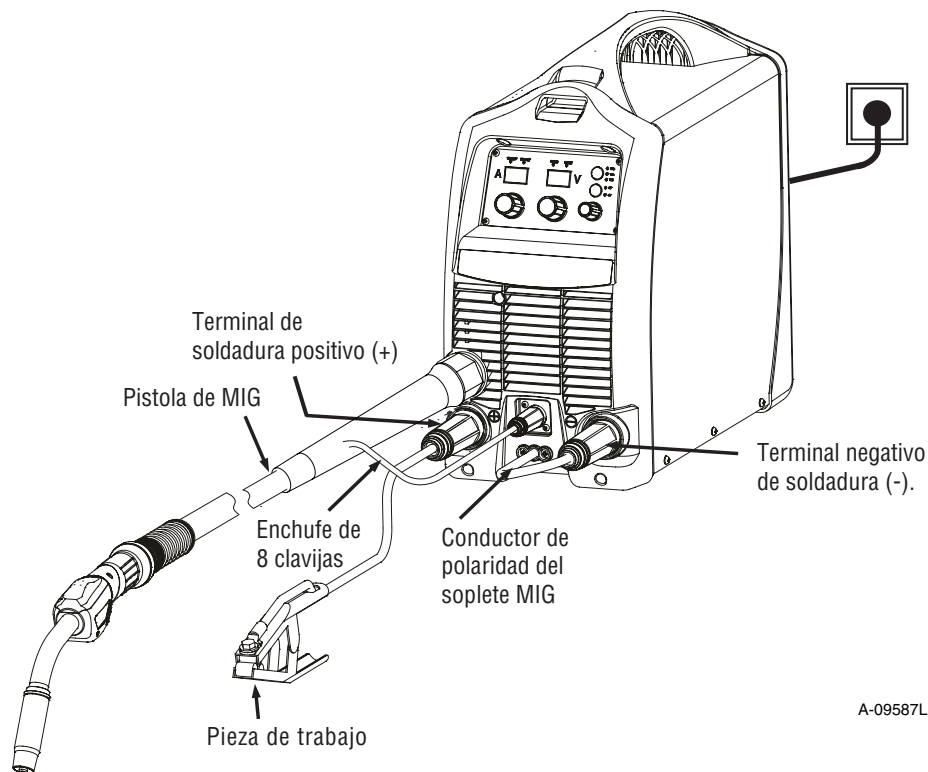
Configuración de la soldadura MIG (FCAW) con el alambre MIG sin gas
